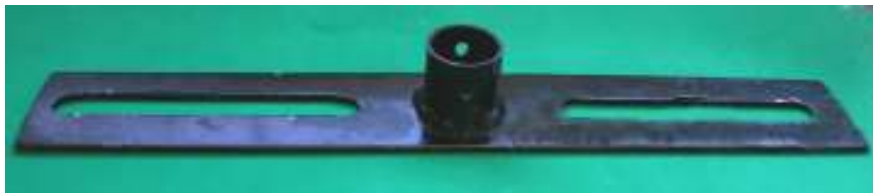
Dispositivo torneado para fixação do tubo de PVC na máquina de teste
